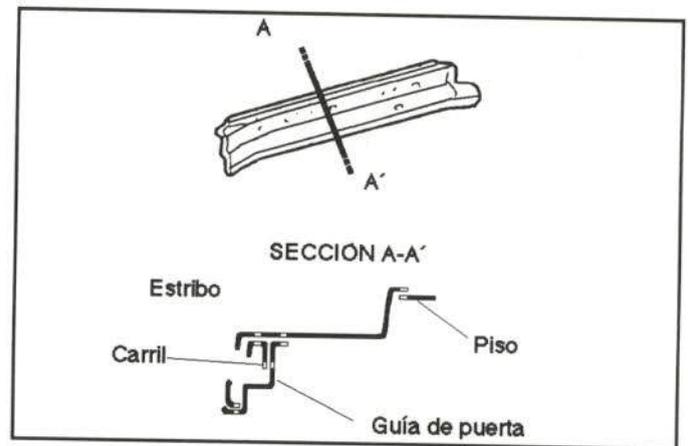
Accesibilidad del estribo bajo puerta lateral
